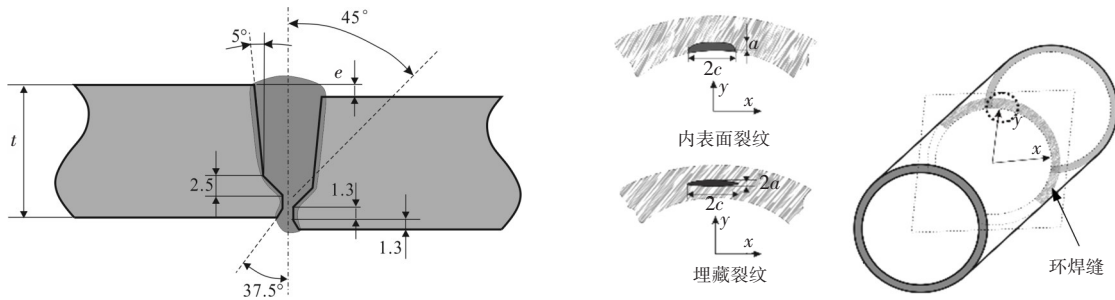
焊缝坡口尺寸及裂纹位置示意图
